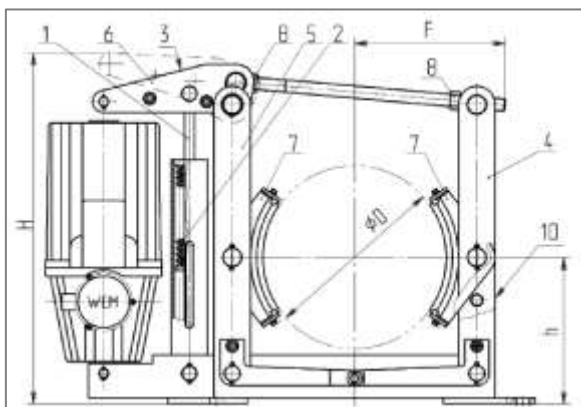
Двухколодочный пружинный тормоз типа ТКГ.
